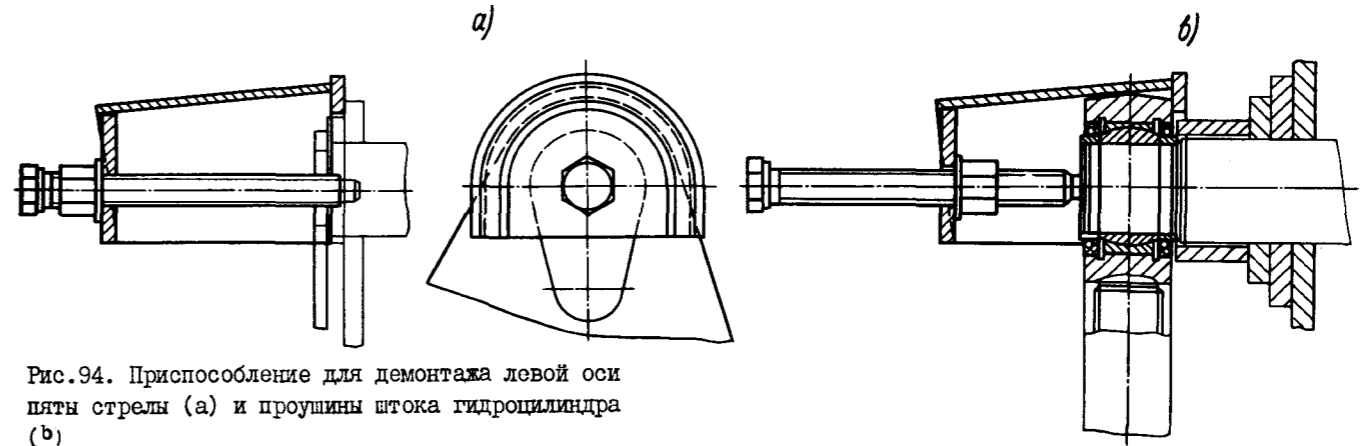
Приспособление для демонтажа левой оси пяти стрелы (а) и проушины штока гидроцилиндра (б)
